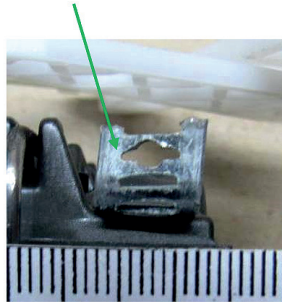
Загальний вигляд внутрішніх поверхонь та механізмів лічильника газу "Ельстер G4" і місця розташування металевої пластини з нашаруванням полімерної речовини чорного кольору (вигляд збоку)
